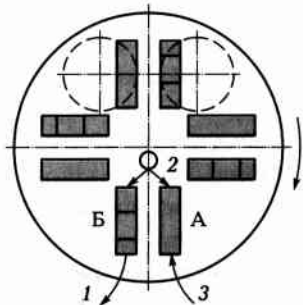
Схема обработки на карусельно-фрезерном станке двух поверхностей заготовки с переустановкой заготовок:
